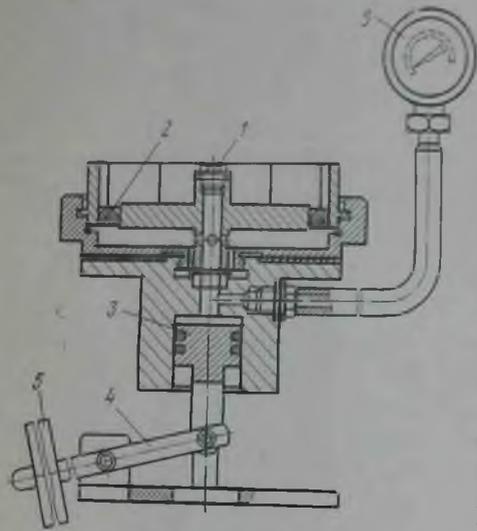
Приспособление для испытания герметичности резиновых манжет
